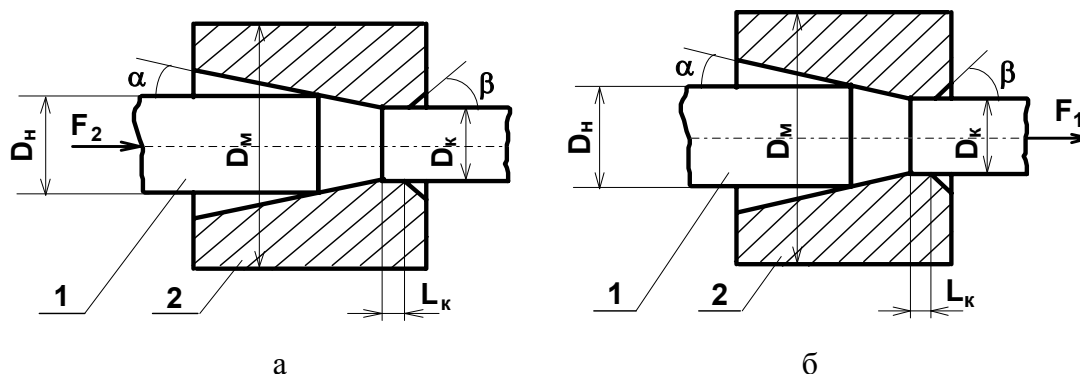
Технологические схемы охватывающего деформирования по схеме сжатия (а) и растяжения (б) заготовки (1 – заготовка; 2 – матрица)
